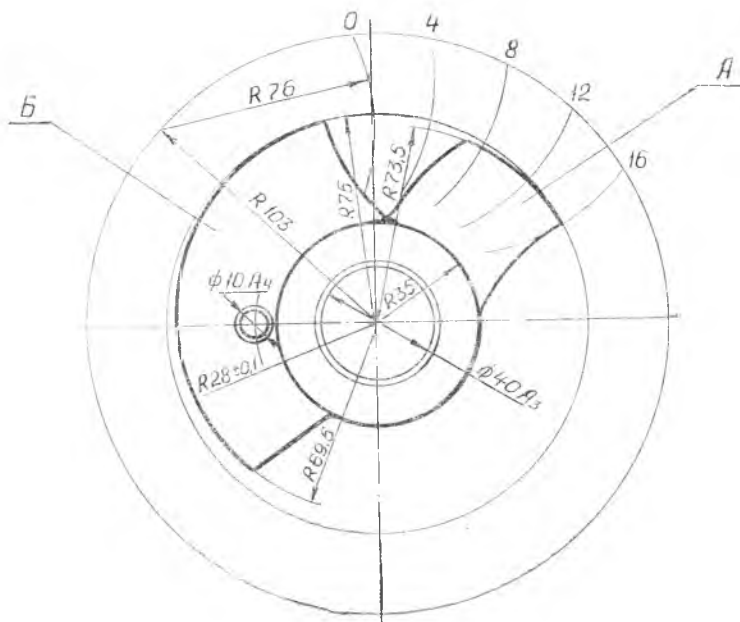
Кулачки поперечных суппортов: А—переднего суппорта для подрезки фаски; Б—заднего суппорта для отрезки детали
